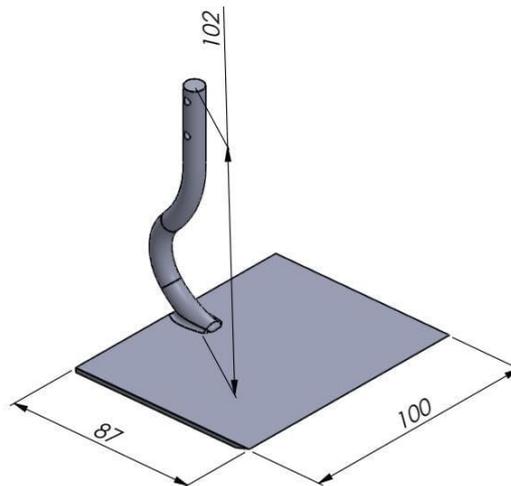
Desenho técnico da enxada de mão, vista lateral.
